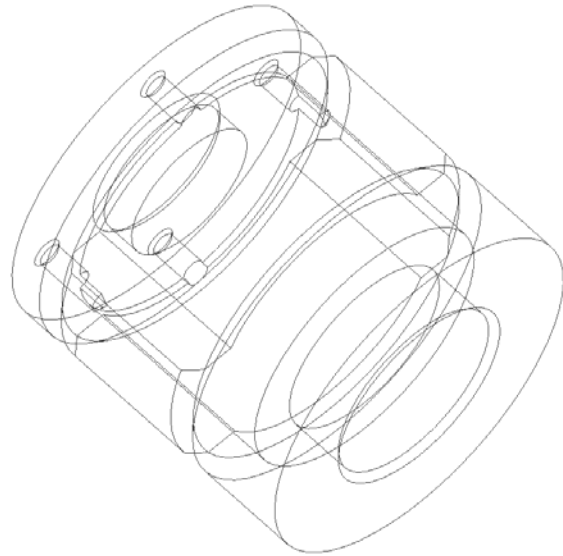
Деталь «Корпус» в каркасном изображении.
